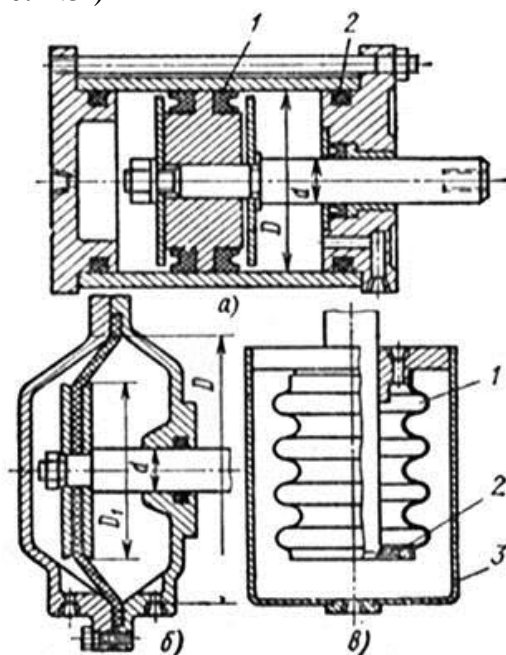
Типы пневмодвигателей с поступательным движением вала
